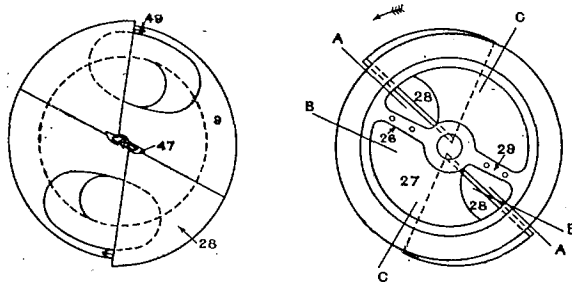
Plan des couteaux du niveau de l'appareil de découpage.
